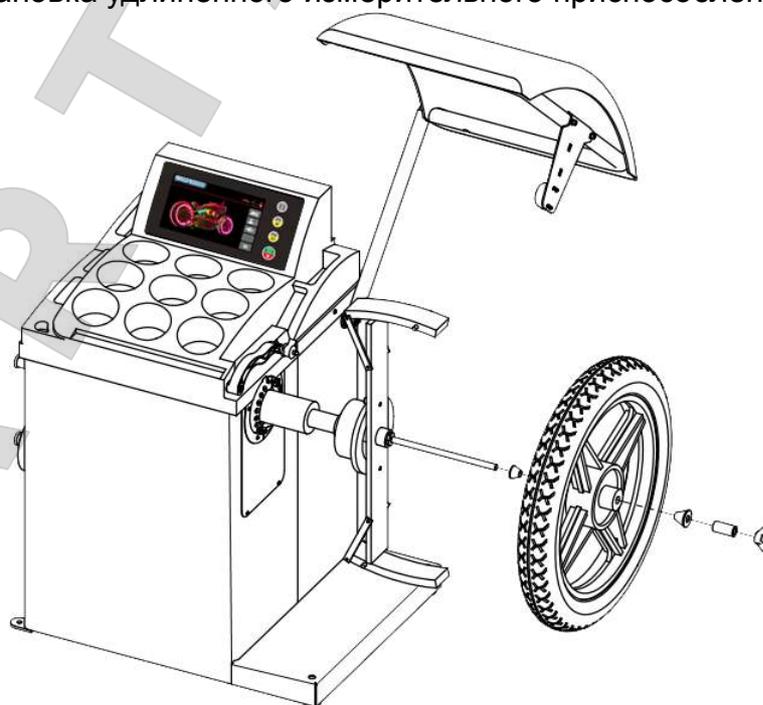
Установка приспособлений, предназначенных для мотоциклов
